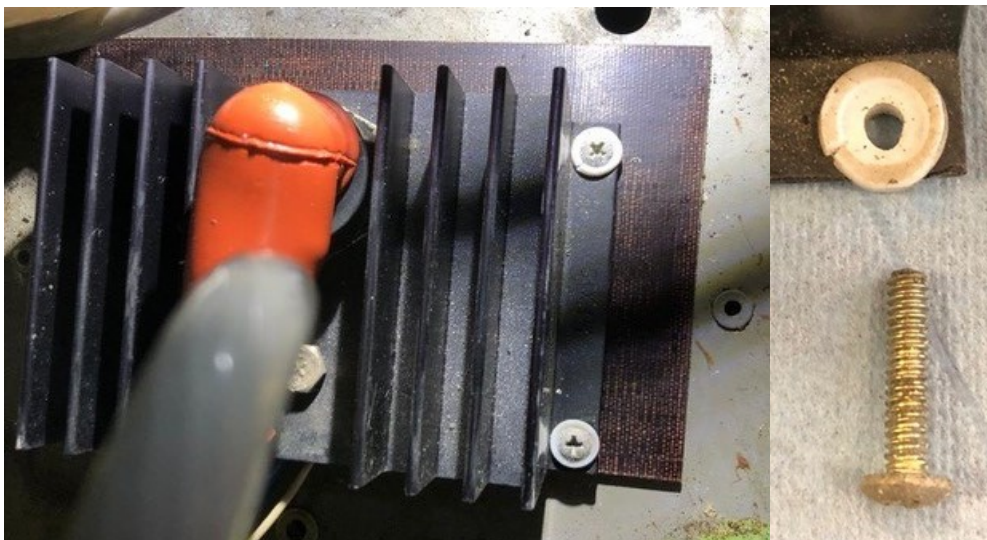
dispositif à diodes monté sur le plancher de l'avion HB-PPB et collerette supérieure de l'une des rondelles isolantes fissurées (Source : BEA)
